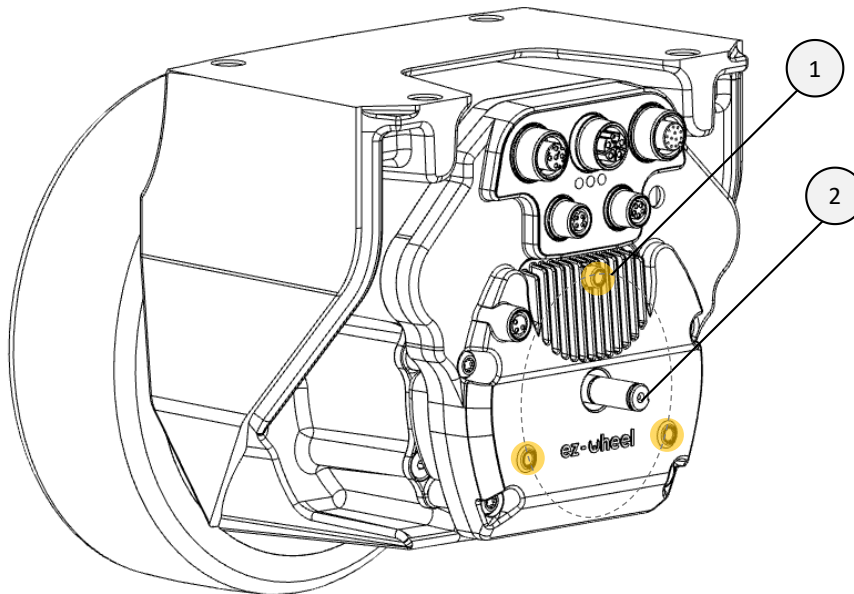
Vue d'ensemble des interfaces mécaniques – SWD® 150
